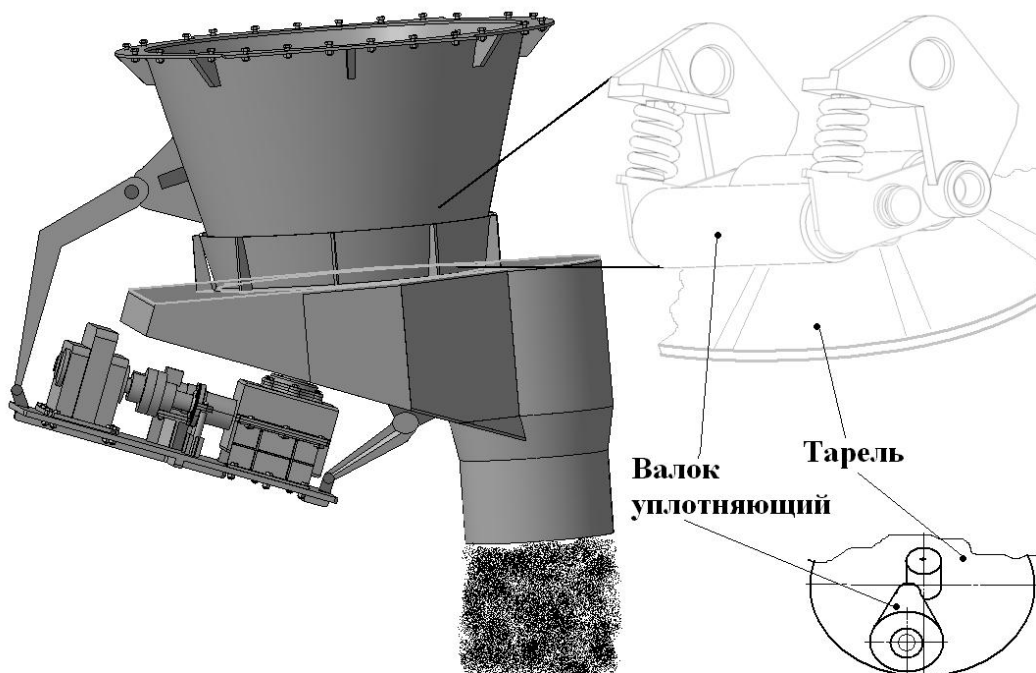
Тарельчатый питатель углезагрузочной машины с подпрессовкой материала между валком и тарелью.
